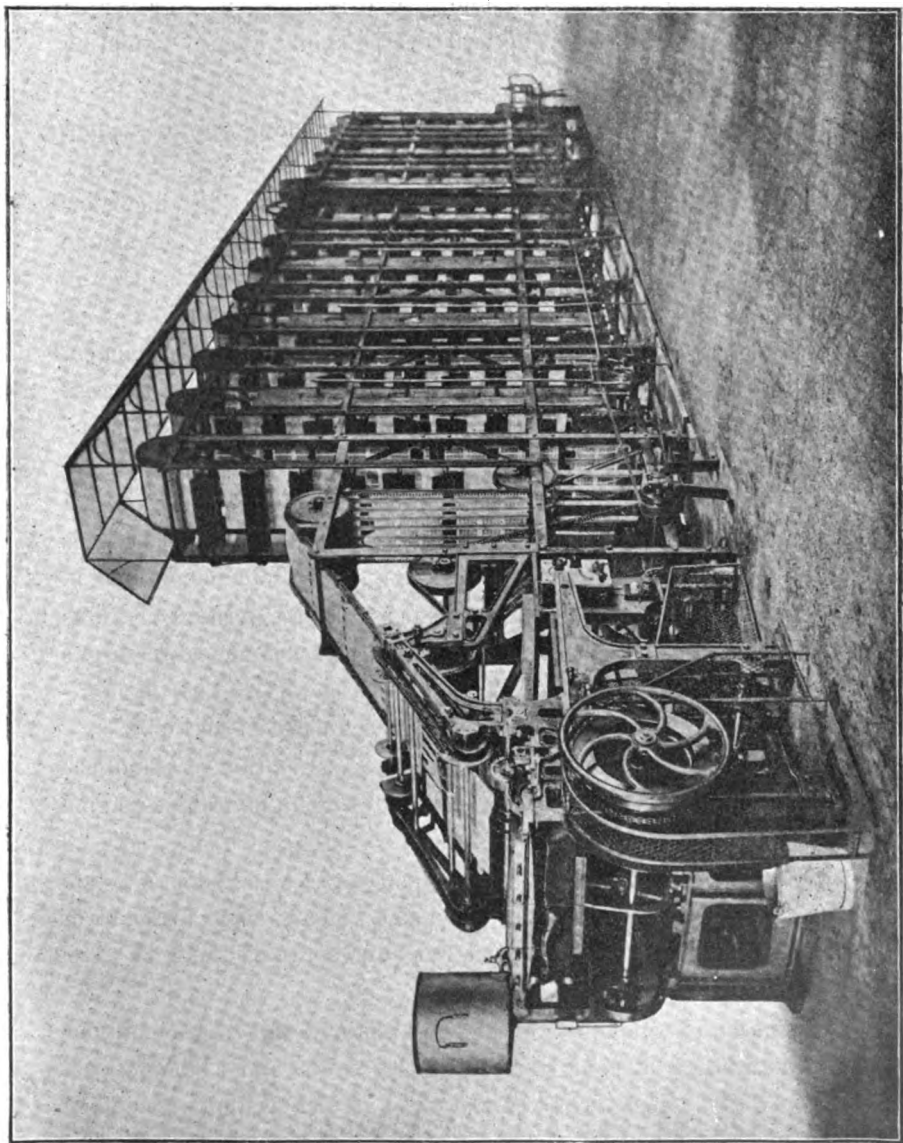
Machine à gommer avec séchoir mécanique : Vue d'ensemble.
